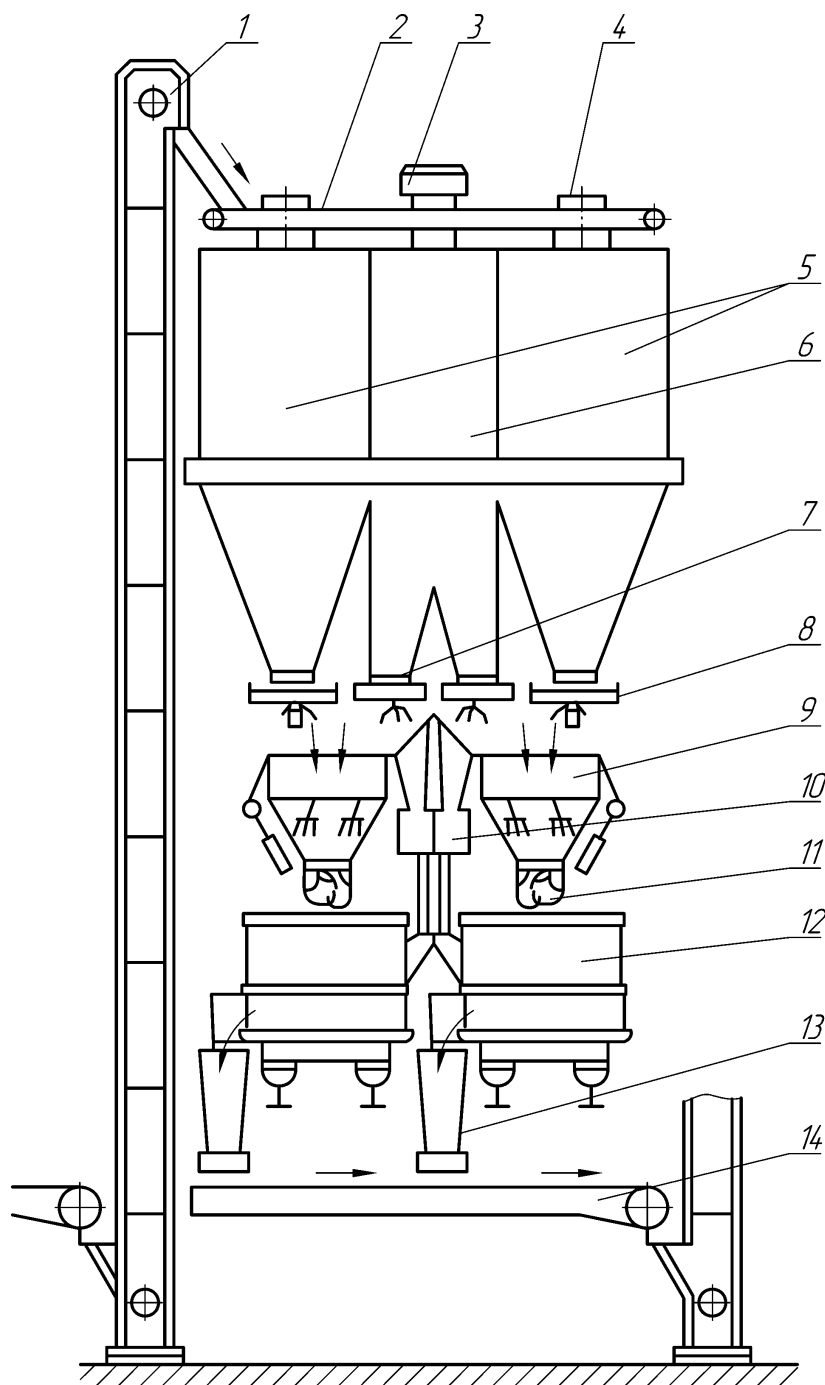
Схема смесеприготовительной установки чугунолитейного цеха ВАЗа
